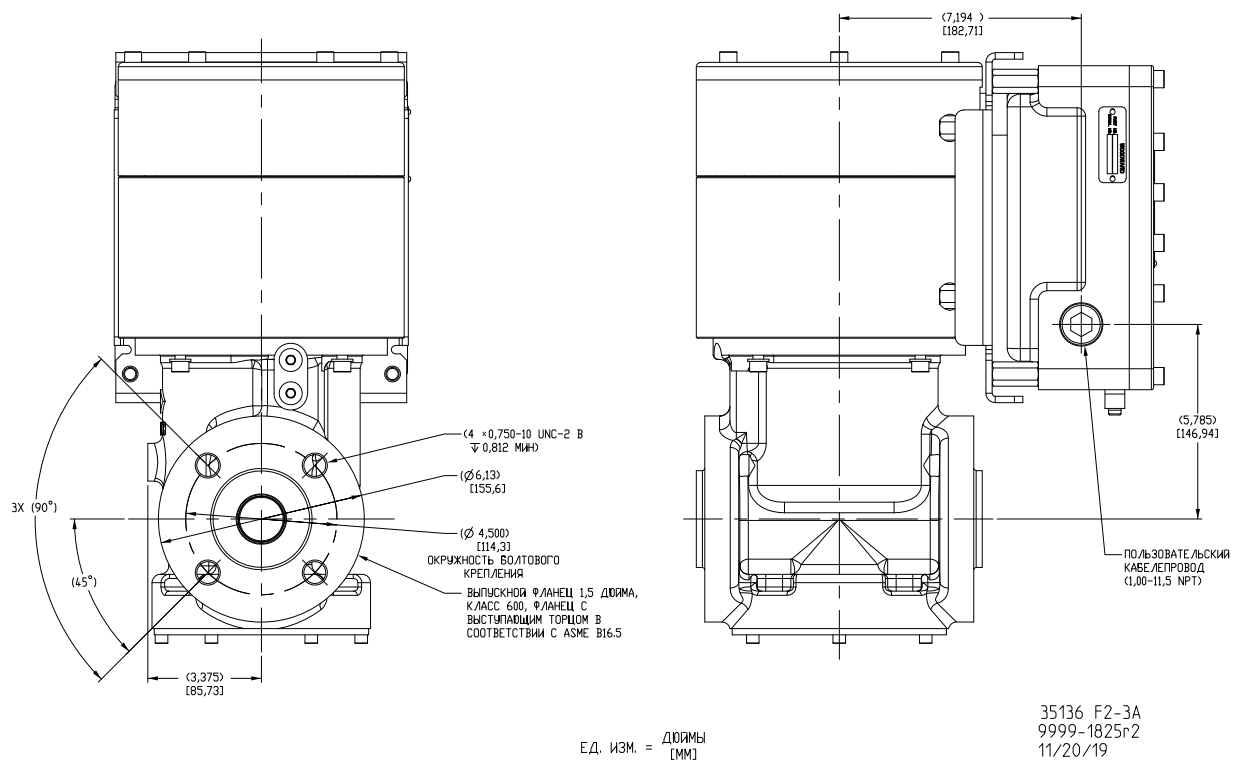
б. Габаритно-присоединительный чертеж, нержавеющая сталь, GS40, с кабельными вводами
